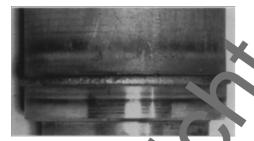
Stauchgrat einer Preßstumpfschweißung an einem Kettenglied;
